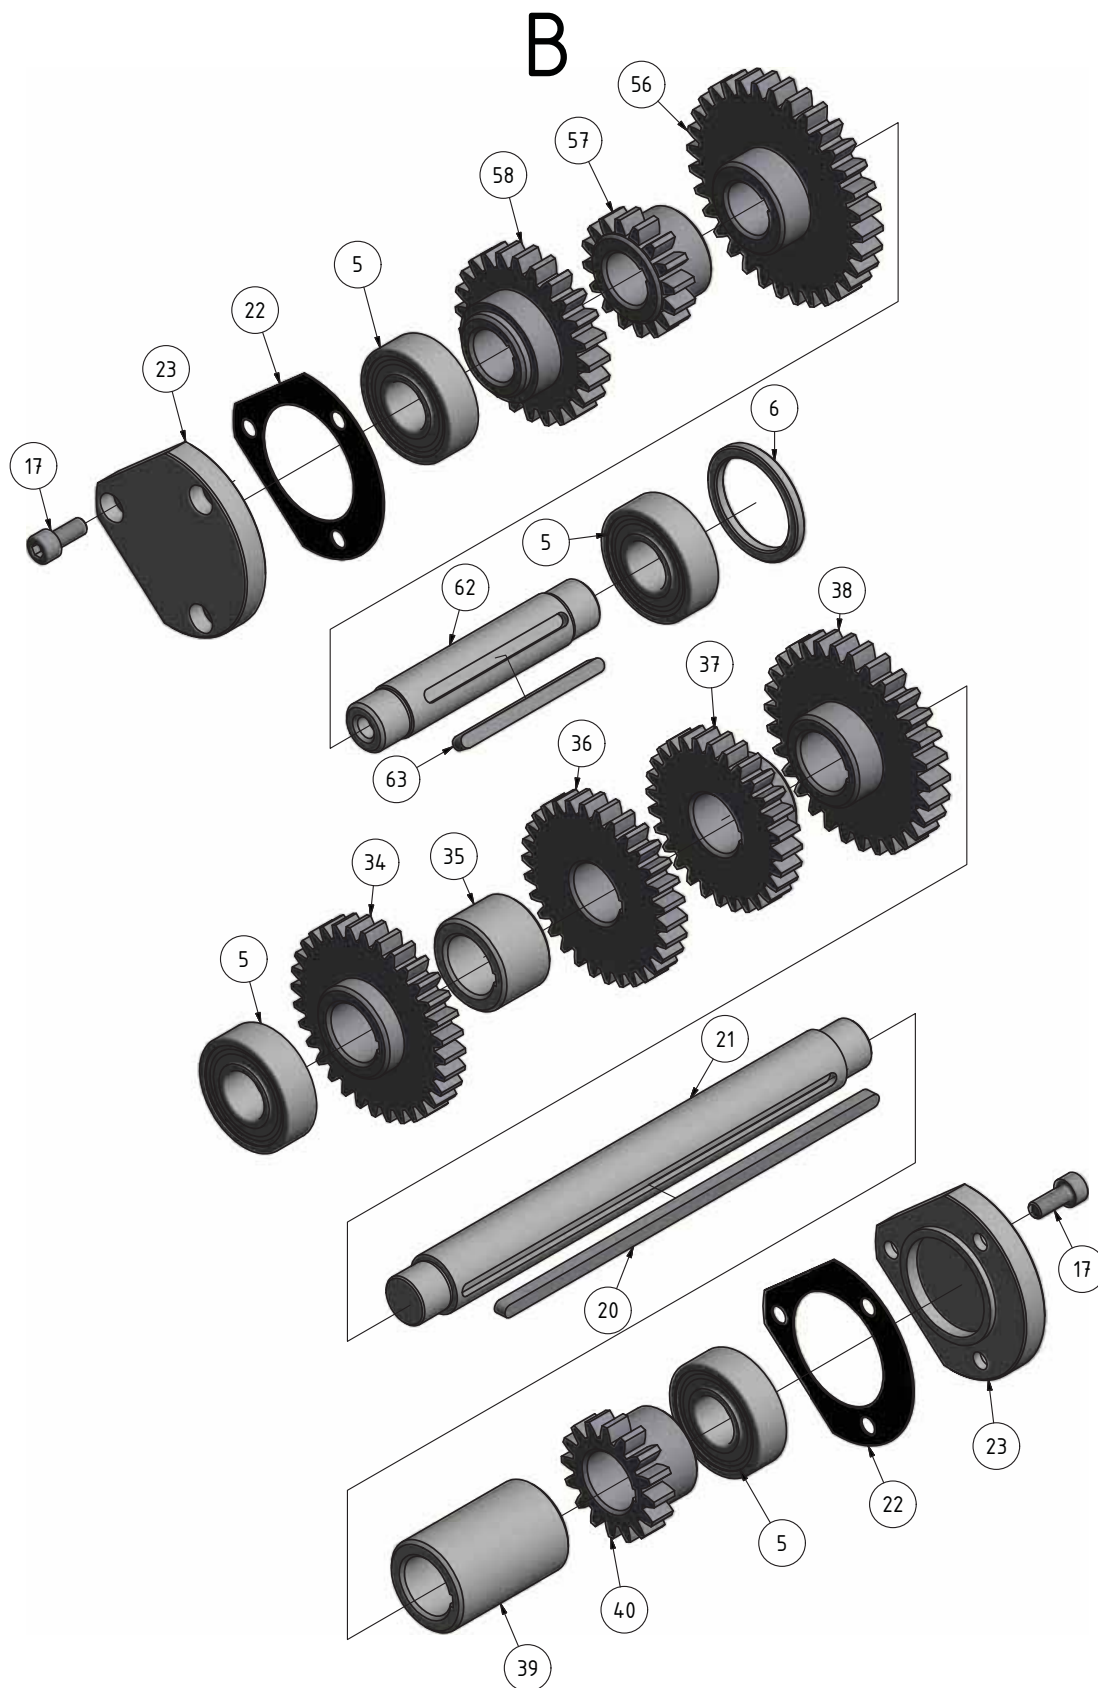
Vorschubgetriebe 4-6 - Feed gear 4-6
